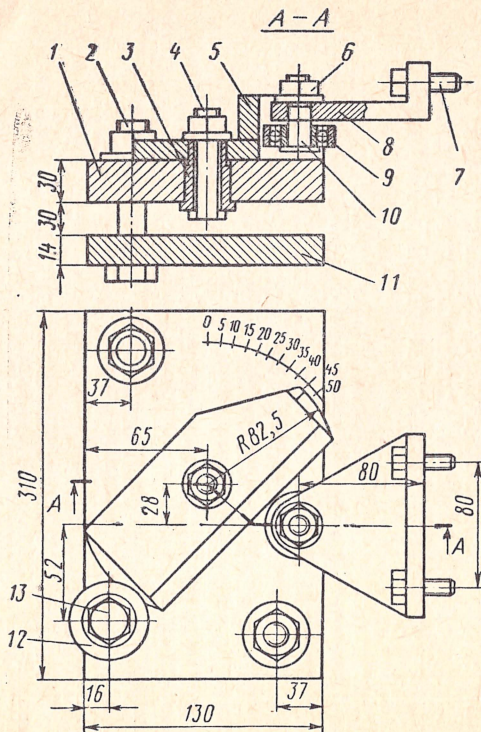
Приспособление для облегчения обработки конических поверхностей деталей на токарном станке
